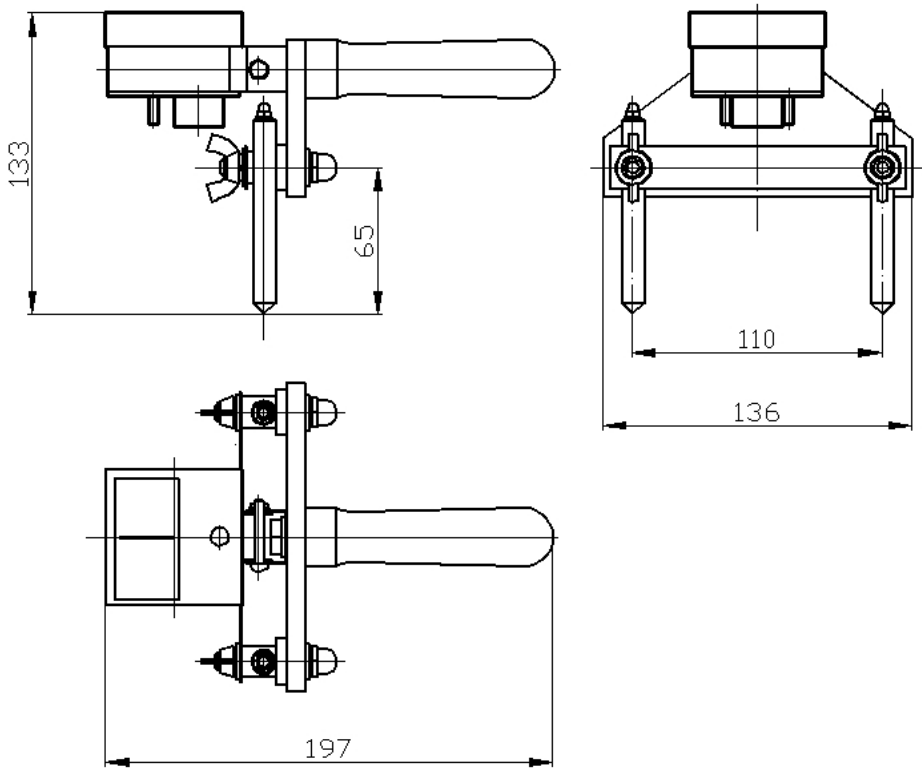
Габаритные размеры вилки нагрузочной НМ-300Э.
